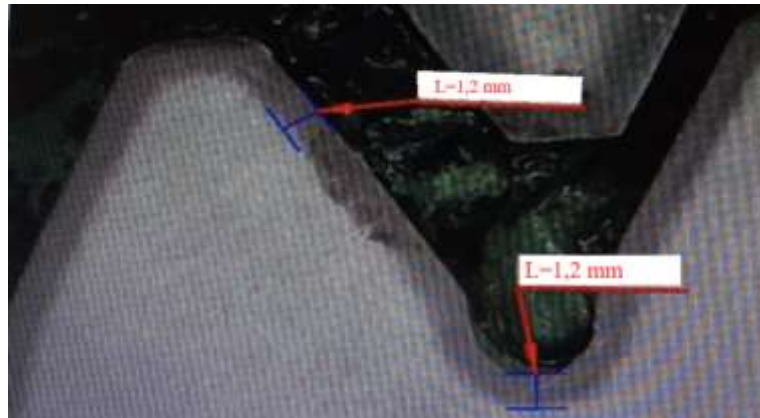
Цементований шар на поверхні зубців деталі, x10.
